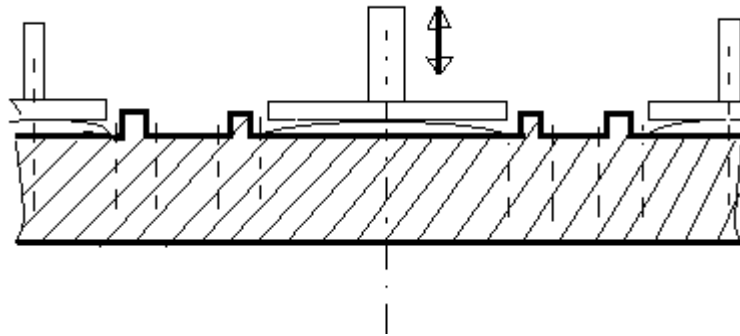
Pistons, aide au démoulage, pour pièce plats
